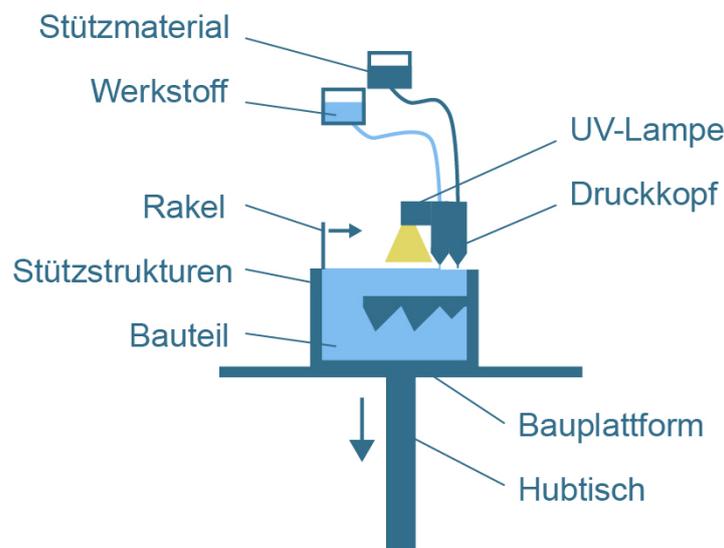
Aufbau und Elemente einer PJM-Anlage
